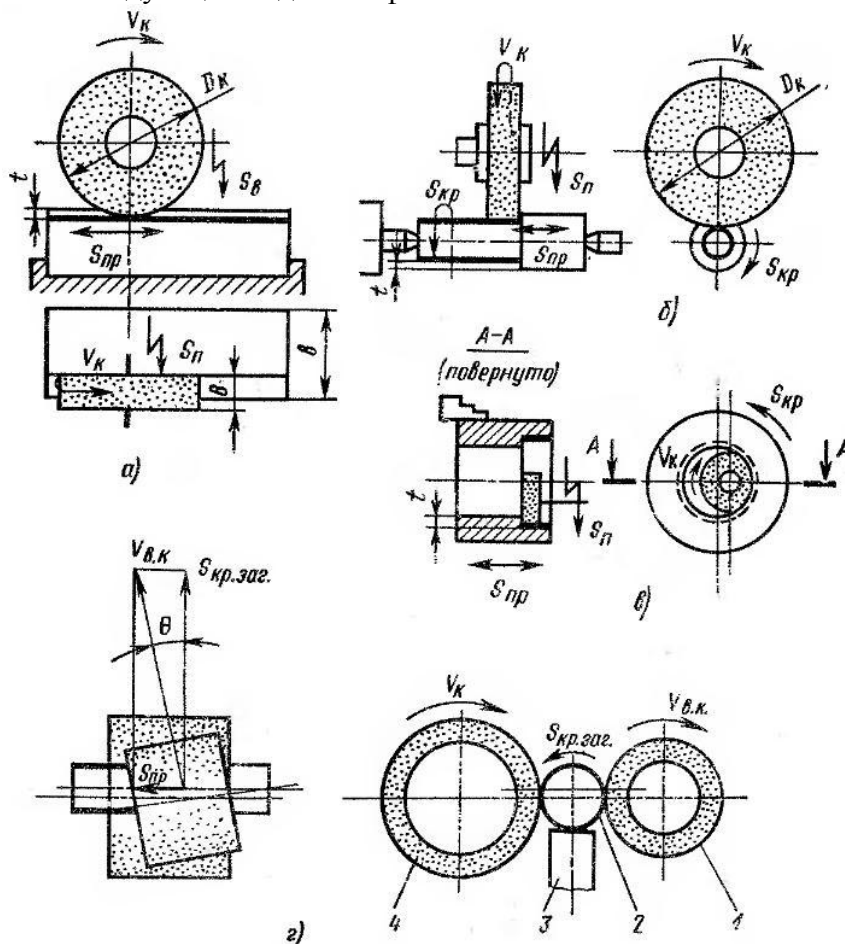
Схемы шлифования: а- плоское, б - наружное круглое; в – внутреннее круглое; г – бесцентровое круглое
